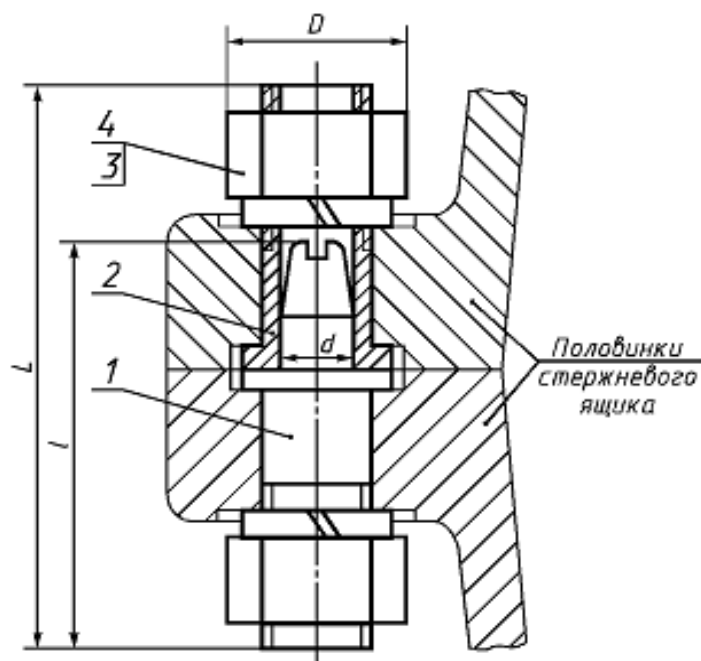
Конструкция соединения штырями и втулками с резьбовыми хвостовиками
